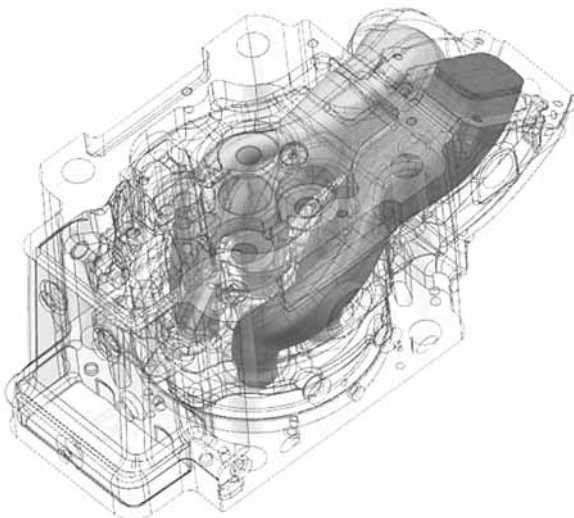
Схема устройства и расположения газовых/воздушных патрубков двигателя ДМ-185
